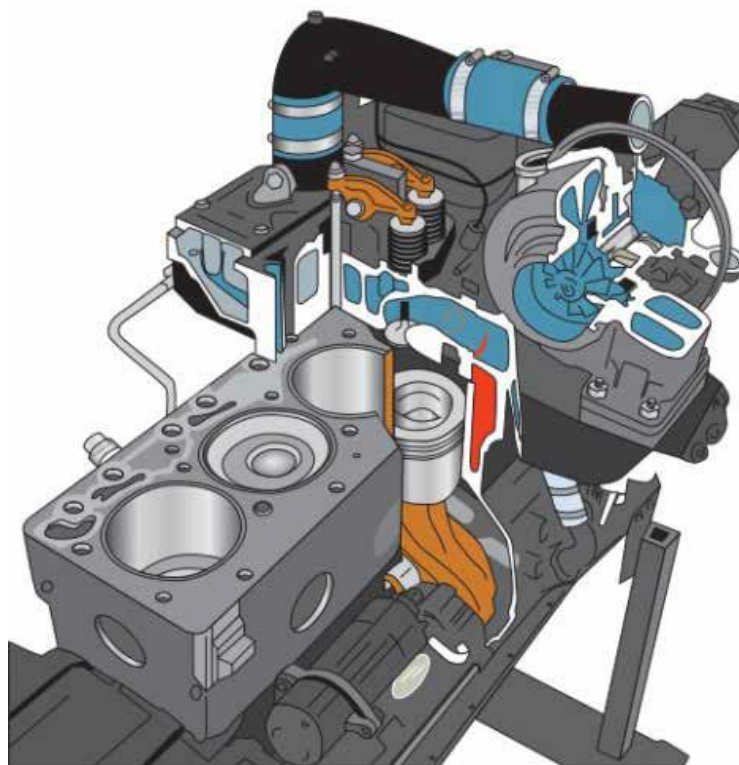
Частичный разрез дизельного двигателя Cummins.
